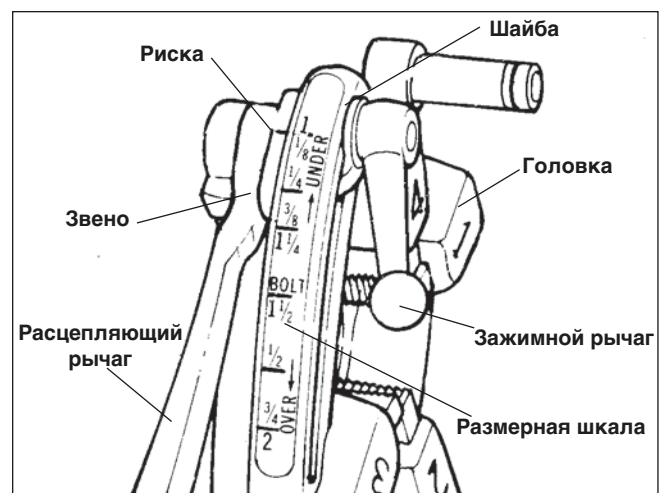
Универсальная быстрооткрывающаяся головка
